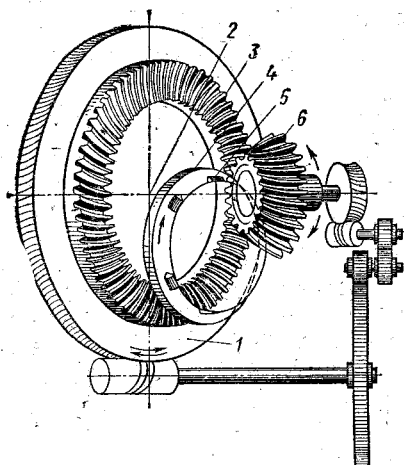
Схема нарезания конических колес с круговыми зубьями резцовыми головками по методу обкатки
